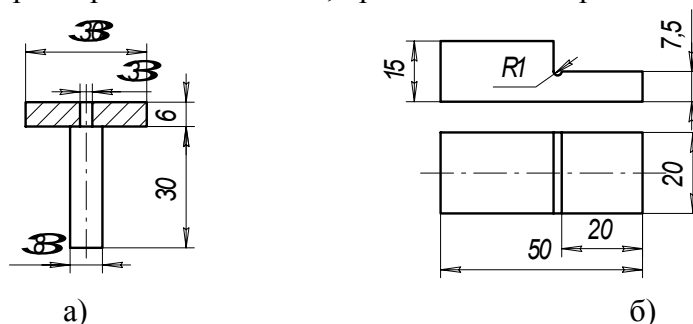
Основные размеры приспособлений для испытания полимерных покрытий
